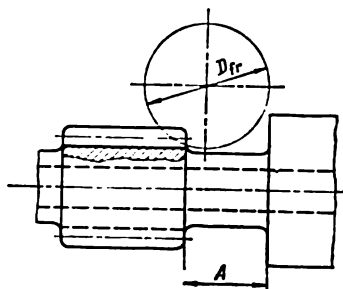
Construction d'une pièce assurant le dégagement de la fraise
